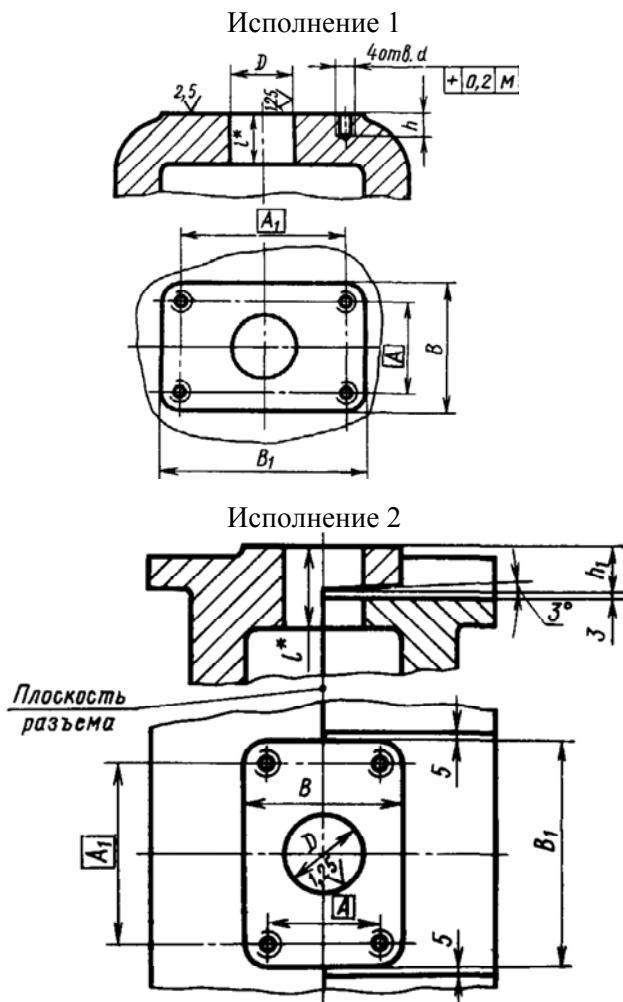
Конструкция платиков для установки пневматического приспособления.
